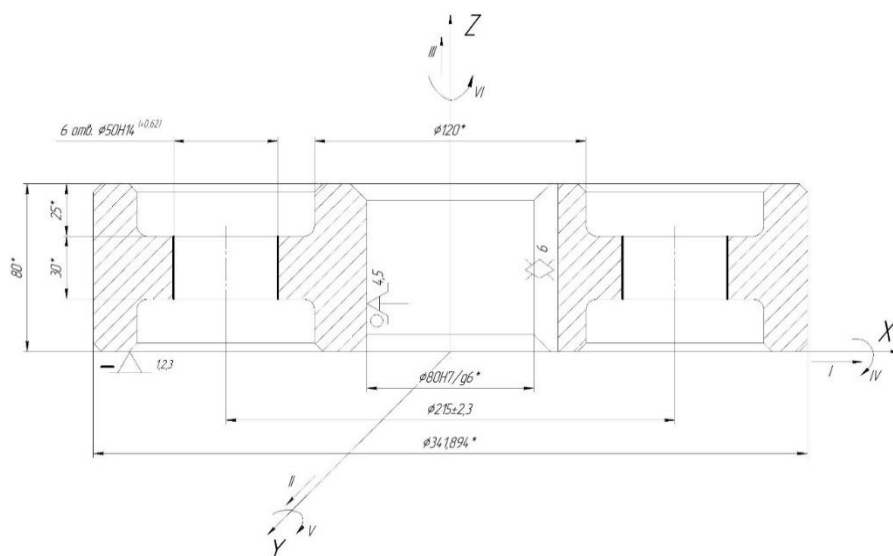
Схема базування заготовки на операції 030 свердлильна з ЧПК
